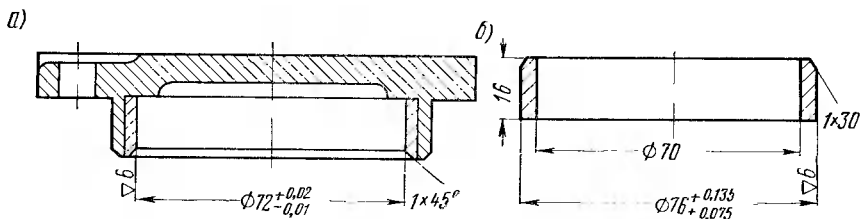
Ремонт гнезда в нижней крышке картера рулевого механизма под наружное кольцо подшипника:
